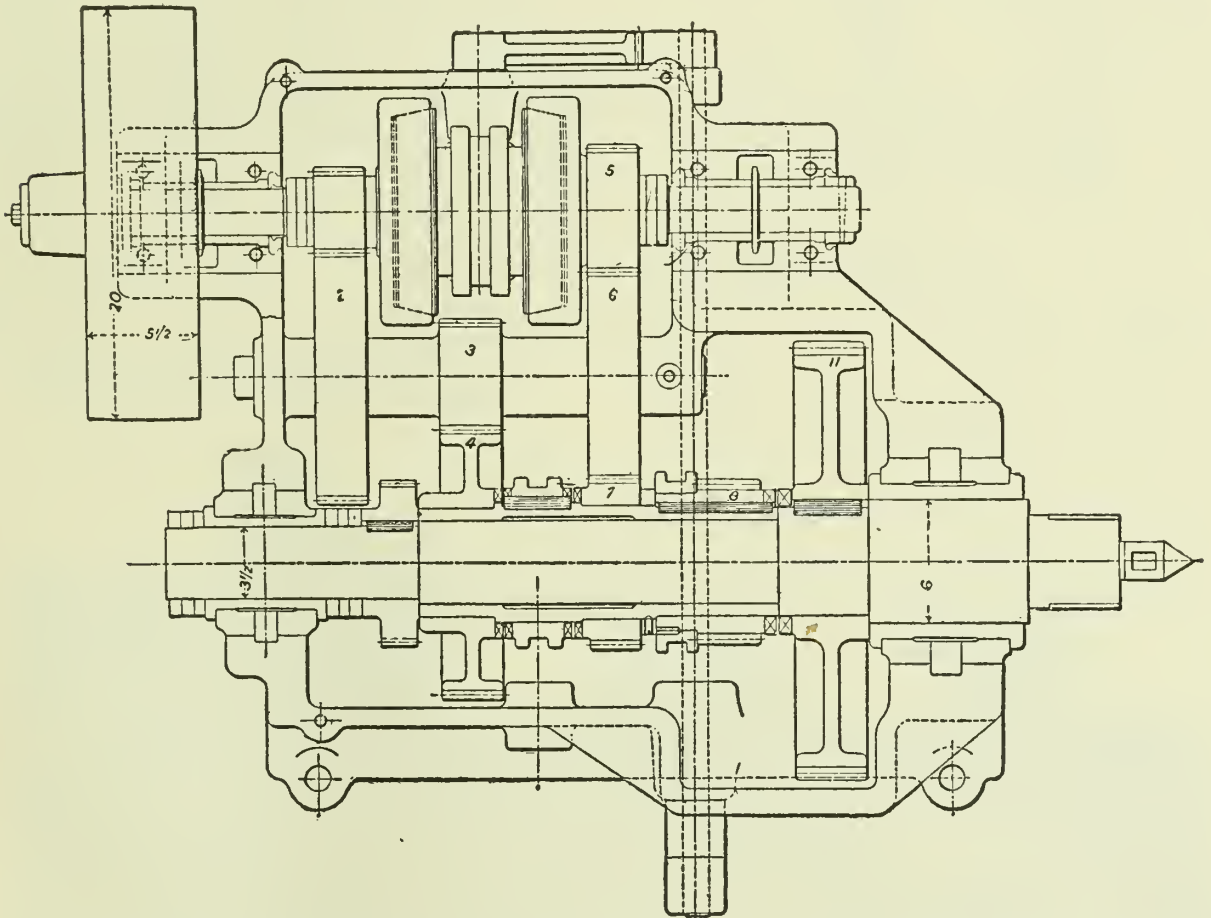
12" Spindelstock der Tangye tool Co. in Birmingham. (Nach „The Engineer“ Machine Tool Suppl. 1904.)
